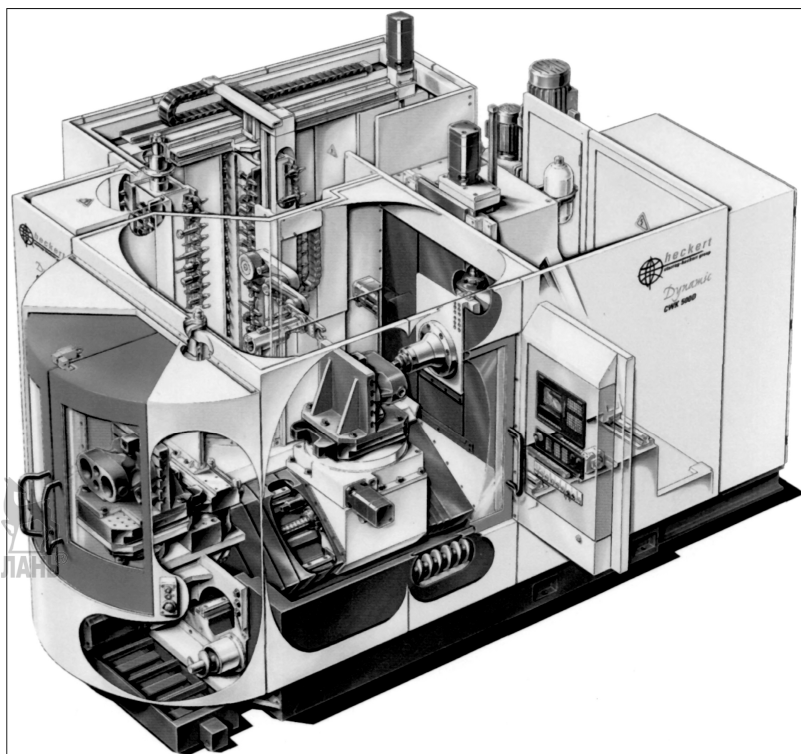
Машинно-обрабатывающий центр SWK-400D
